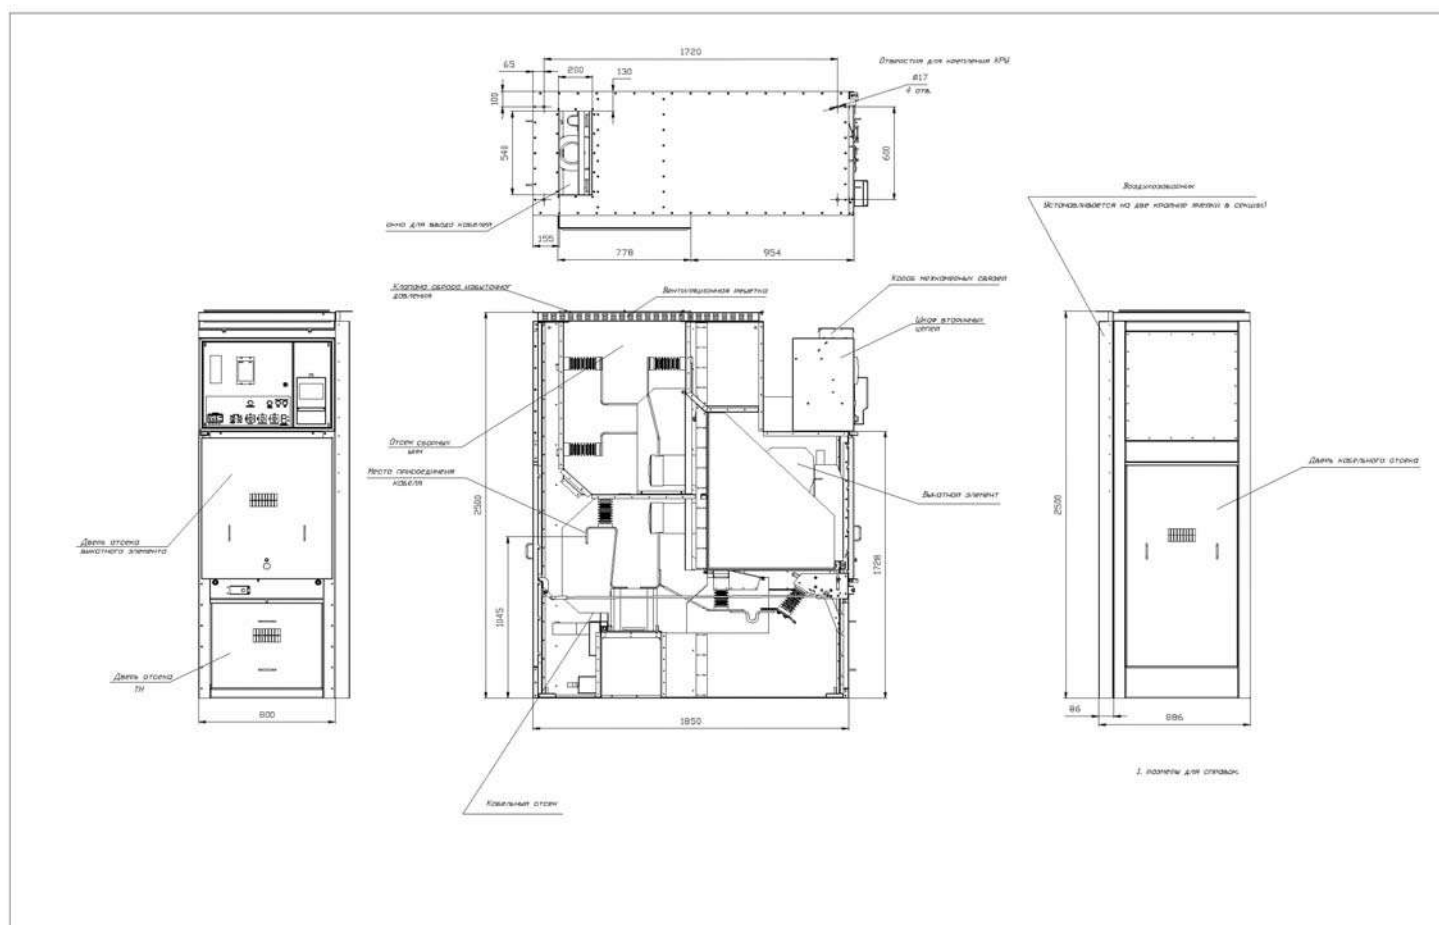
Общий вид и габаритные размеры КРУ2-СТ20
